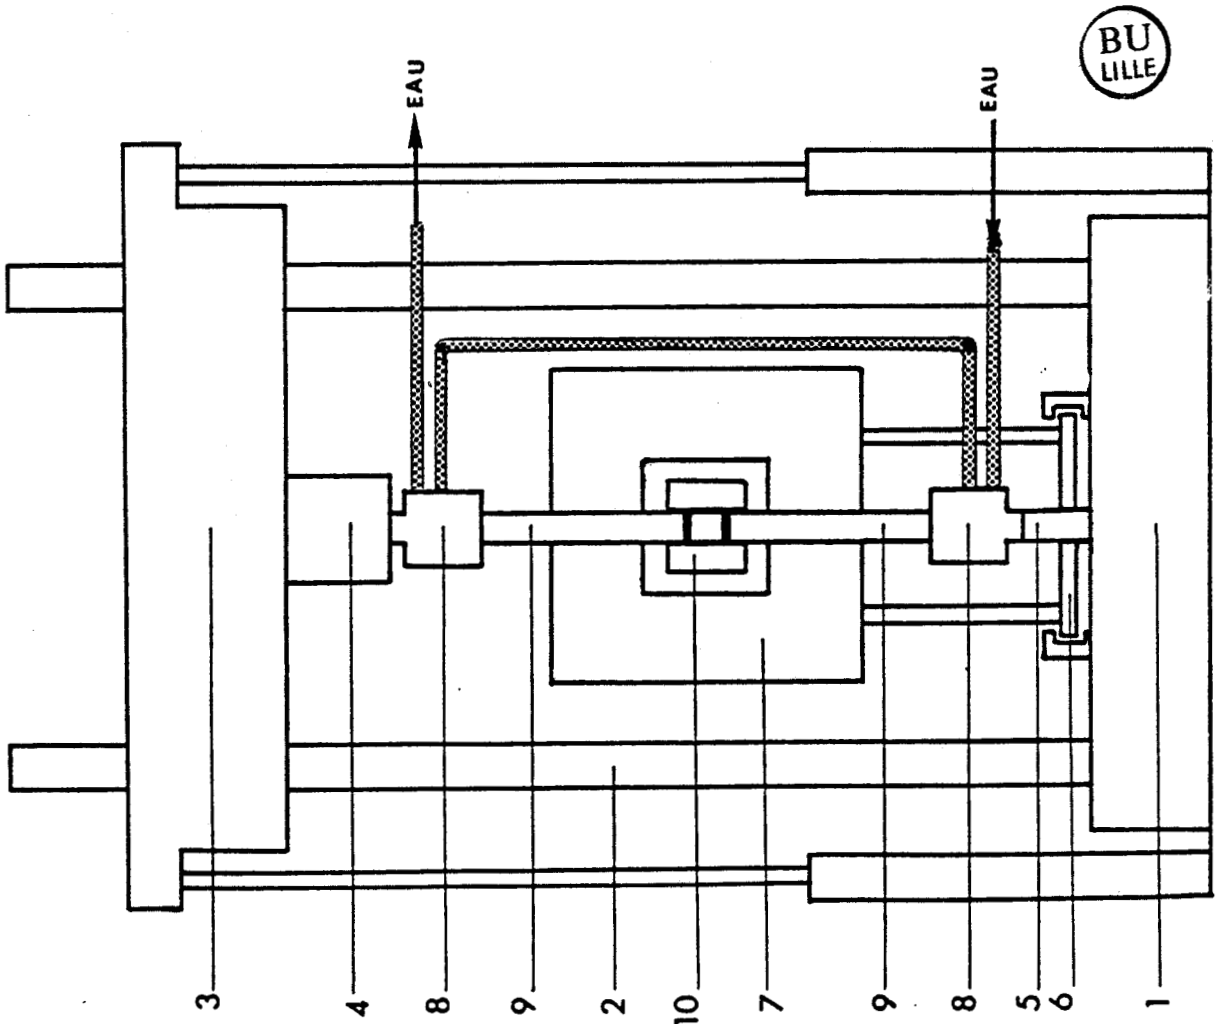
b- : Montage de frittage (sur machine M.T.S.)
